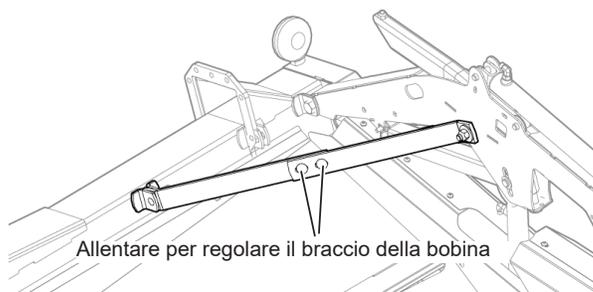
Centraggio bobina - staffa del braccio della bobina terminale
